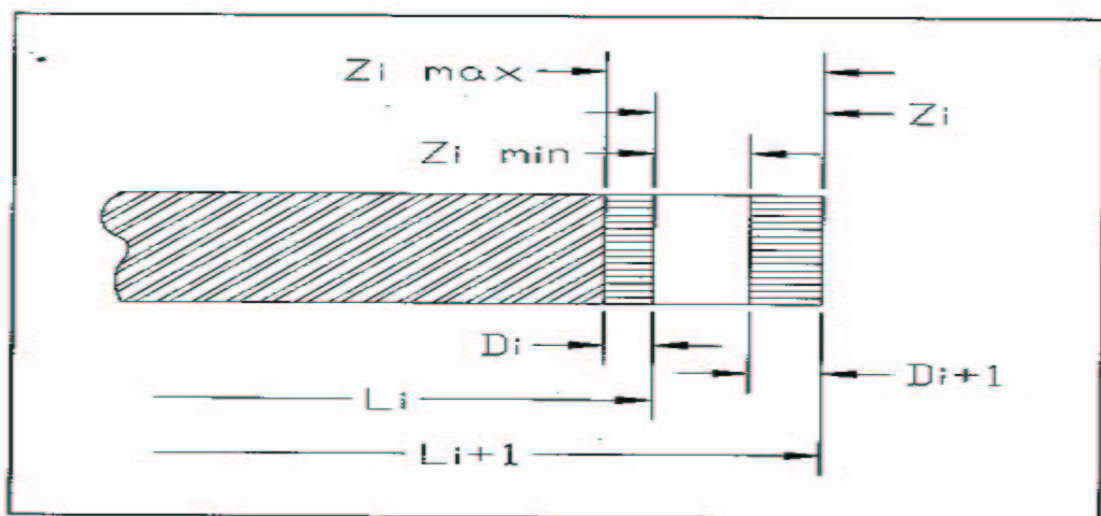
Superfície que será usinada mostrando dimensões e sobre-metal parcial com respectivas tolerâncias.
